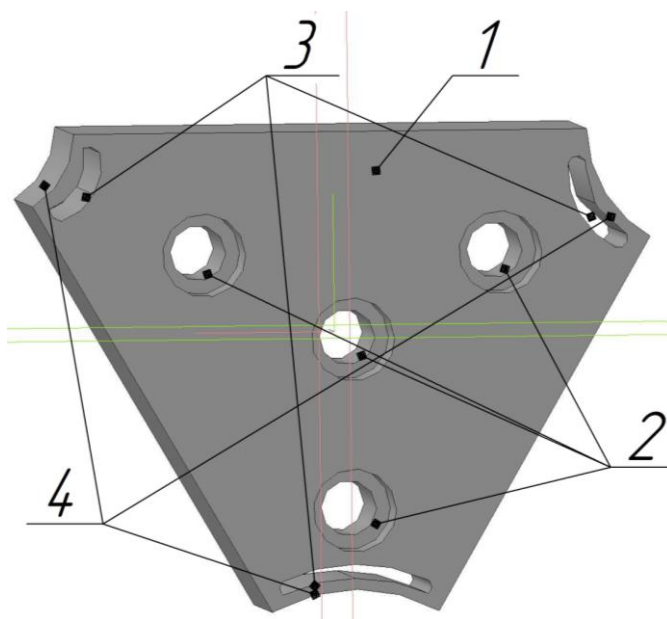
Конструкція адаптивного затискного кулачка для затиску трьох різних діапазонів діаметрів оброблюваних заготовок
